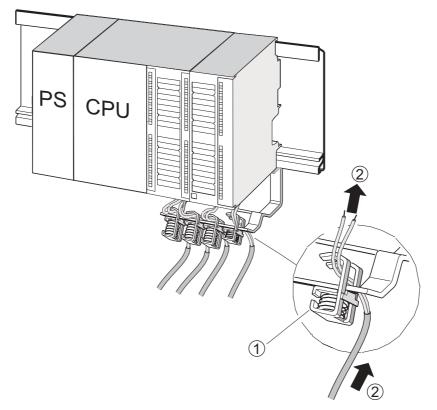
Geschirmte 2-Draht-Leitungen auf Schirmauflageelement auflegen
